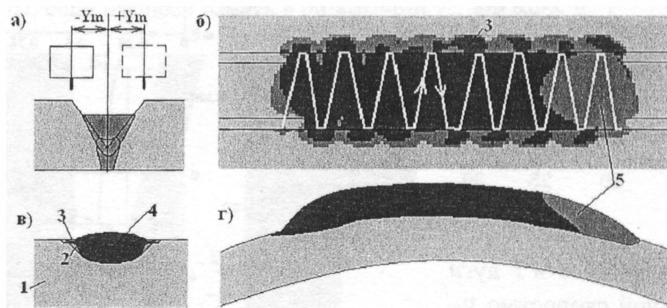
Формирование облицовочного слоя при сварке с поперечными колебаниями горелки: а - разделка кромок; б - вид на стык сверху на начальной стадии сварки; в, г - поперечное и продольное сечение шва по плоскости симметрии стыка (1 - исходный металл; 2 - зона периодического оплавления, 3 - зона поступления основного металла в сварочную ванну 4)
